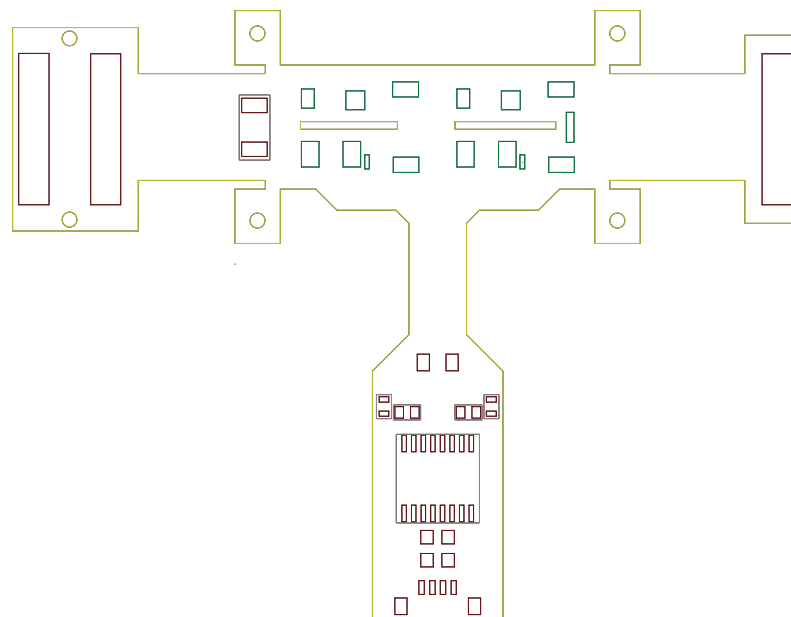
Trilhagem do PCB Flexível – Camada EdgeCuts.
